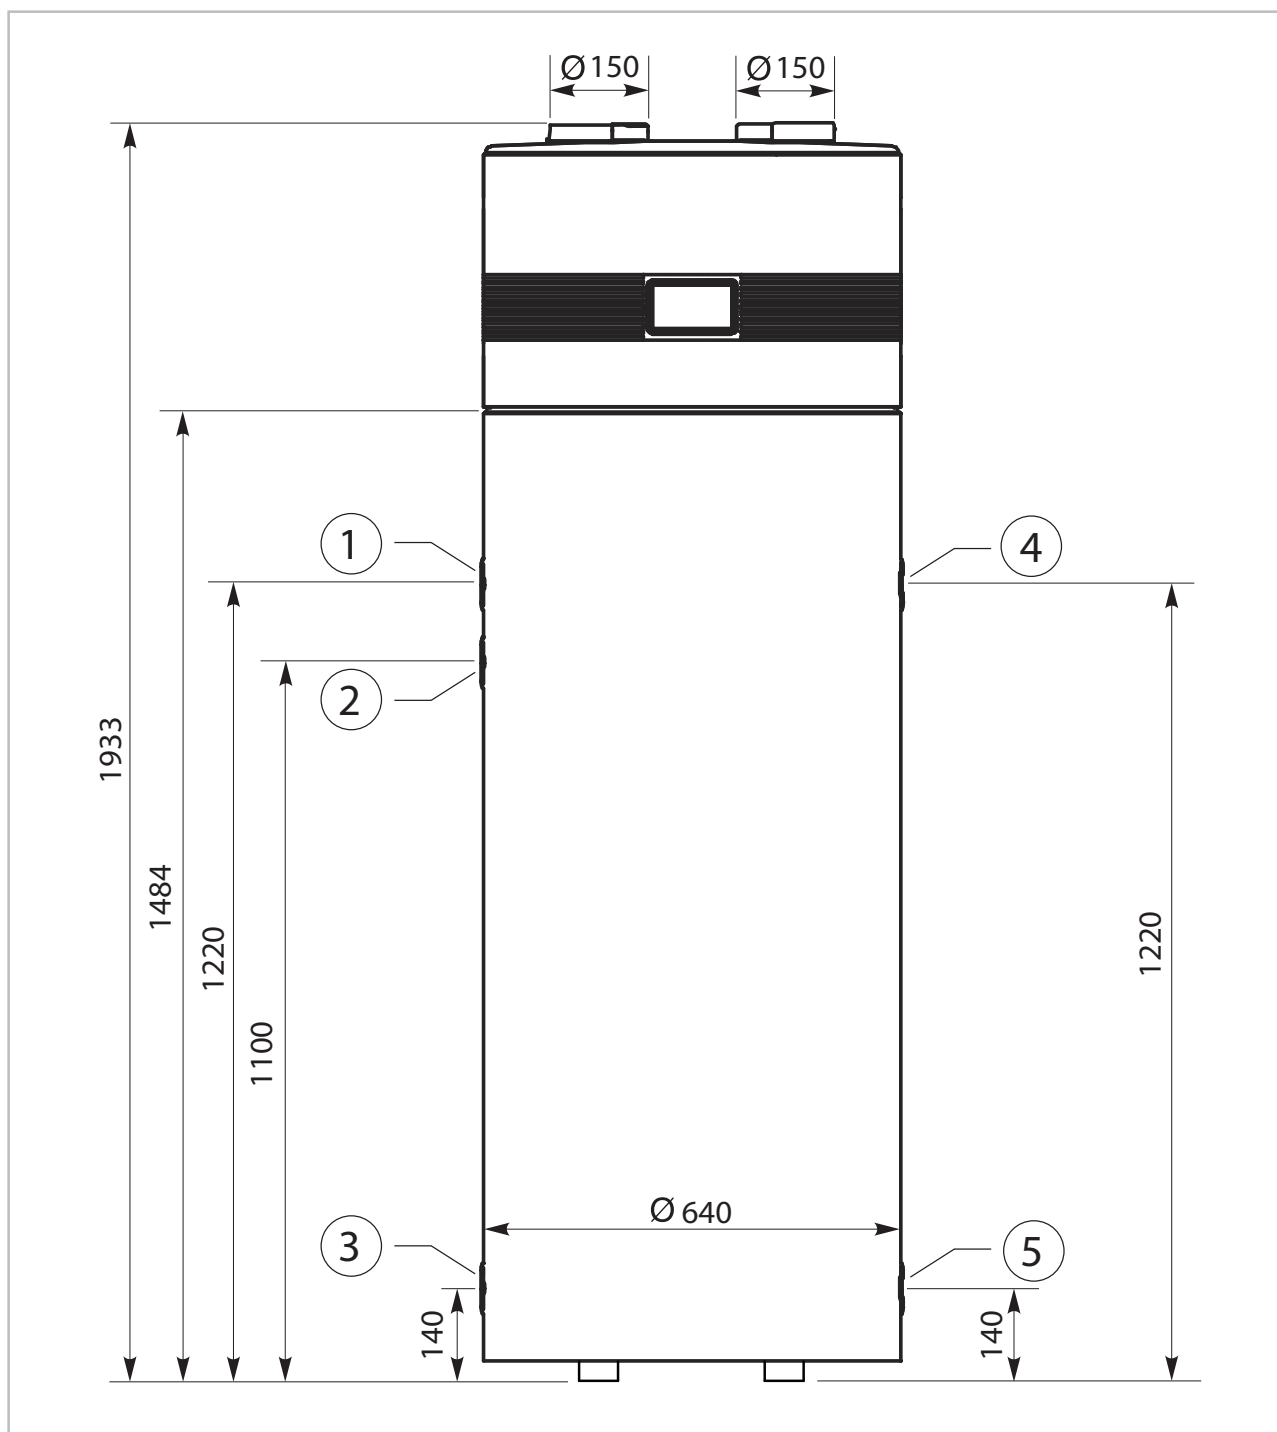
Abmessungen und Bezeichnungen der Rohranschlüsse (Angaben in mm)
